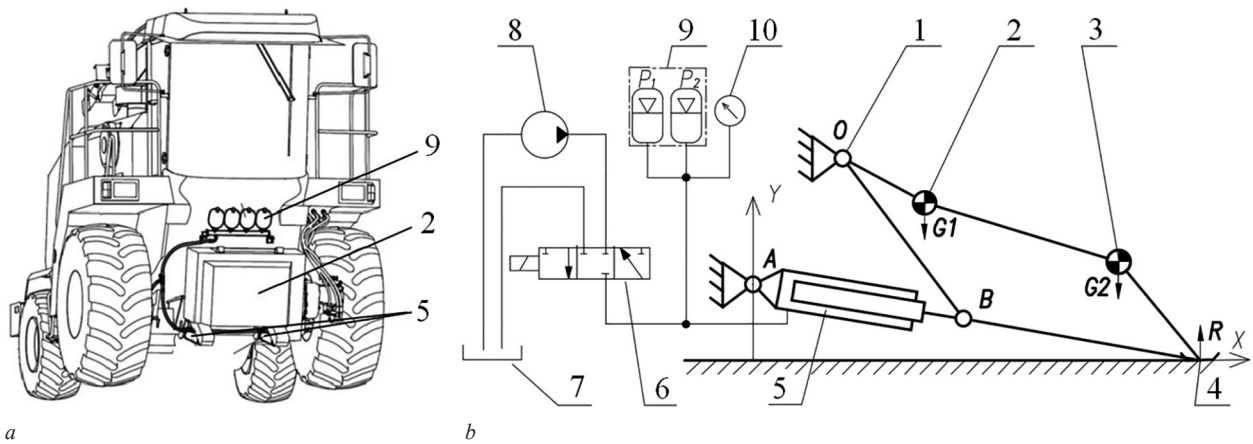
Кормоуборочный комбайн с системой копирования гидропневматического типа:
